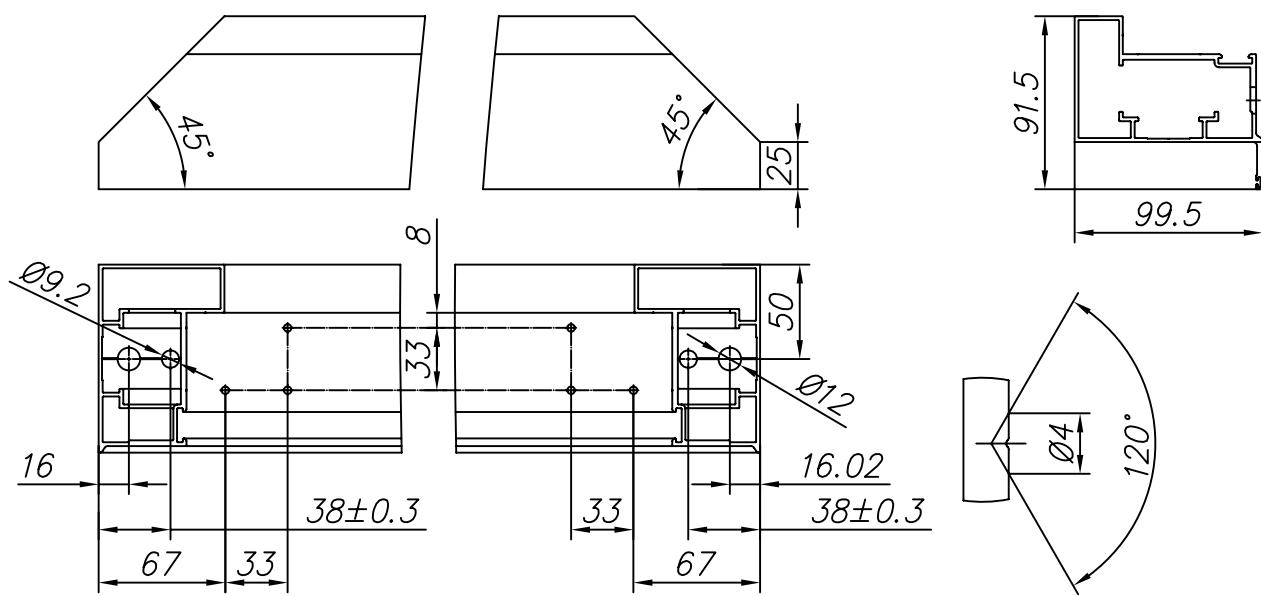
Изготовление стойки (профиль рамы FLGU.400.0106)
